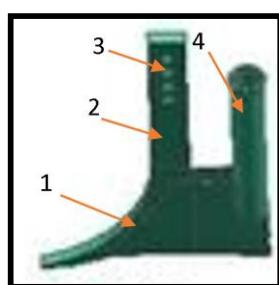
Подкормочное приспособление: 1 – нож; 2 – корпус; 3 - стойка; 3 – распрут.
